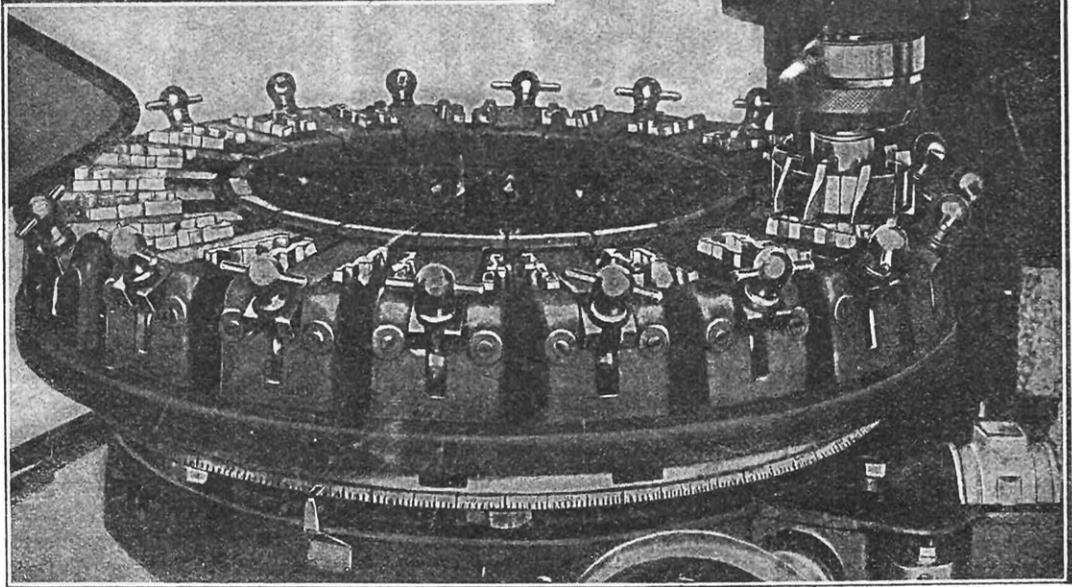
MACHINE A FRAISER PERMETTANT L'USINAGE CONTINU
